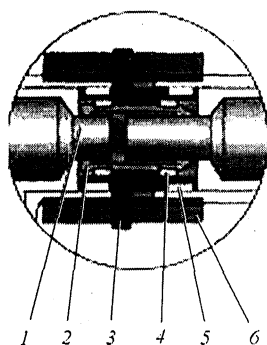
Сборные шины КРУ/TEL: 1 — отрезки сборных шин; 2 — контакты цангового типа; 3 — изоляционная втулка; 4 — разрезные пружины; 5 — резиновые уплотнения; 6 — гайка из полимерного материала
